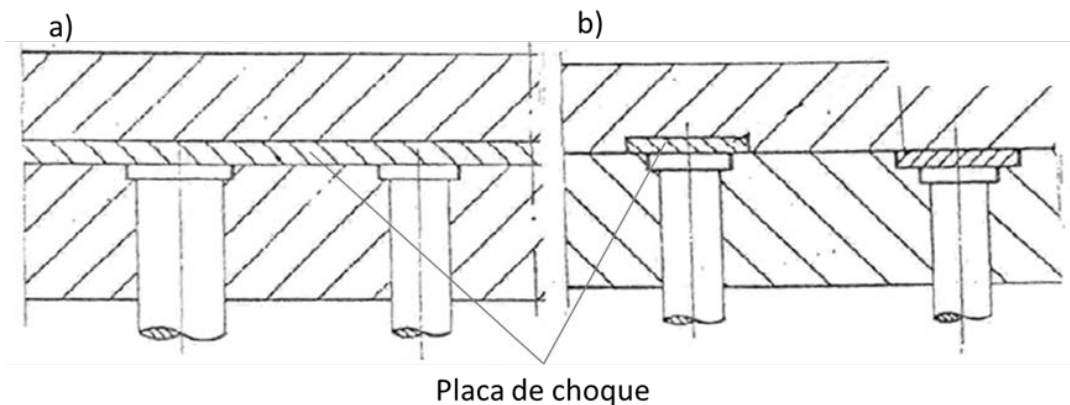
a) Placa de choque Inteira; b) Placa de choque segmentada [11]
